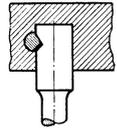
Stempelbefestigung durch abgeflachten Rundkeil.
